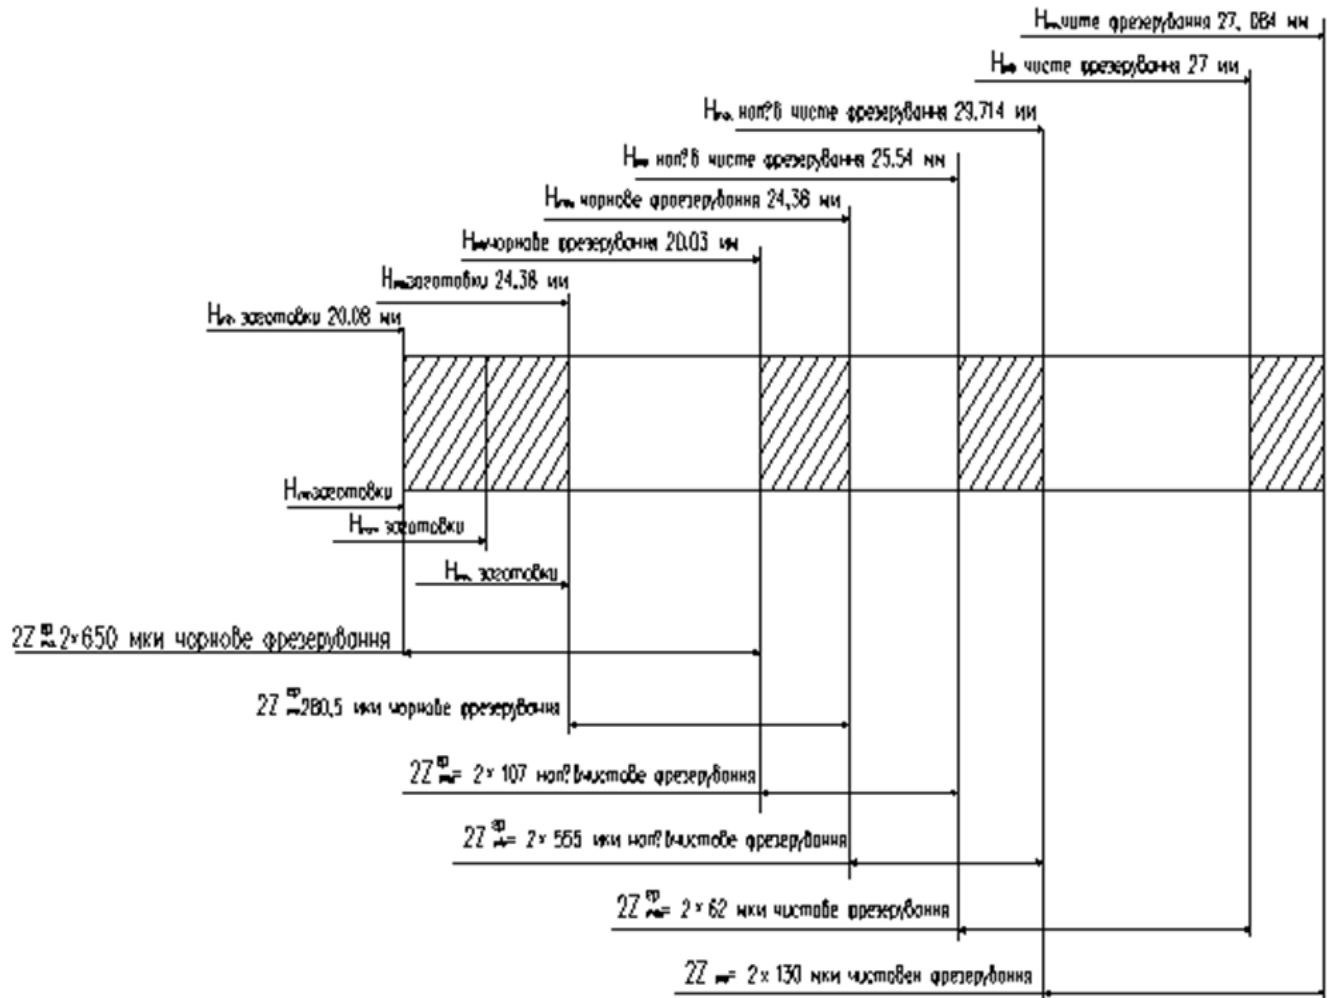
Схема графічного розташування припусків та допусків на обробку пазу 27 H10(+0.084)
